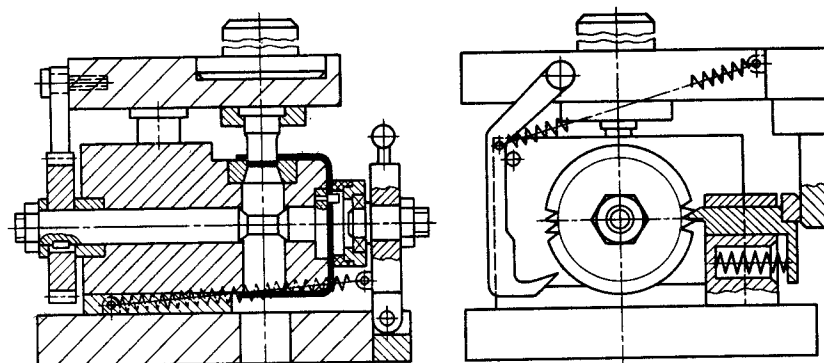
Штампы с поворотным механизмом для пробивки отверстий в цилиндрической детали
